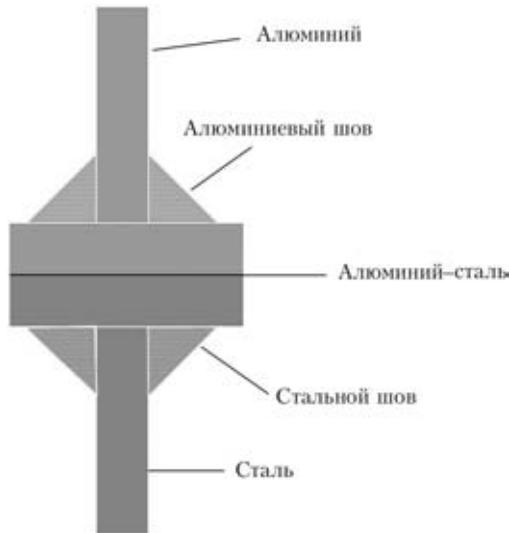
Схема переходника алюминий-сталь, вырезанного из биметалла, полученного сваркой взрывом
